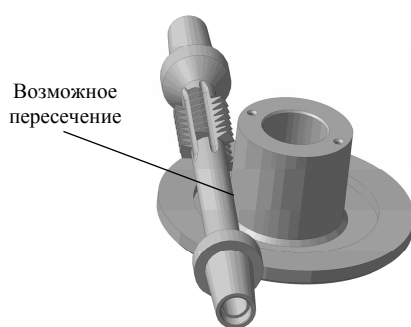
Проверка пересечения ступичной части колеса с телом фрезы
